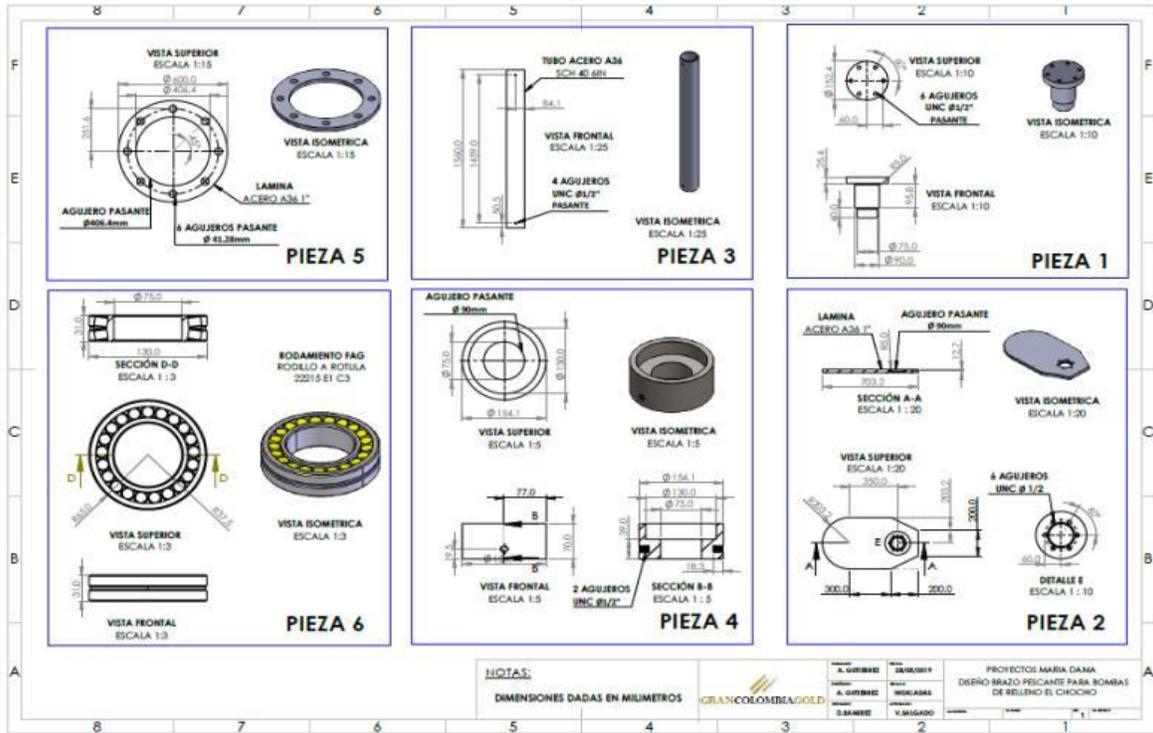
Plano #1 de piezas brazo pescante (Autoría Propia)
